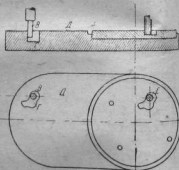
Станок для фрезеровки коротких и длинных пазов.
